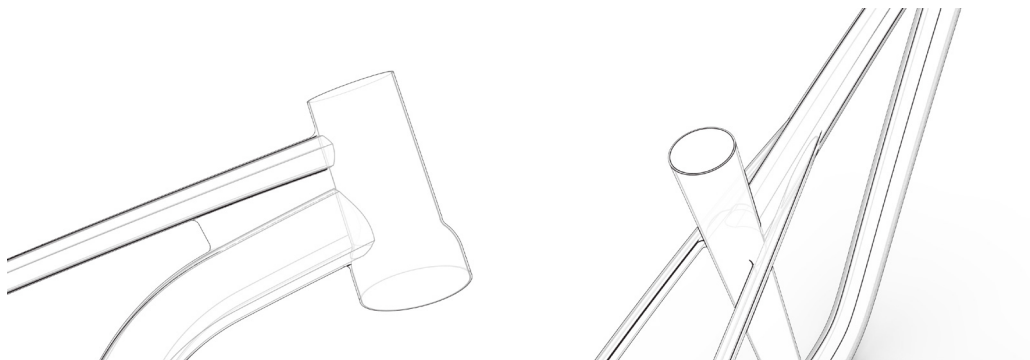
Cordón de soldadura para el refuerzo de tubos superior e inferior. Acero
